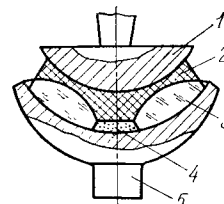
Эластичное крепление деталей заливкой смолы
